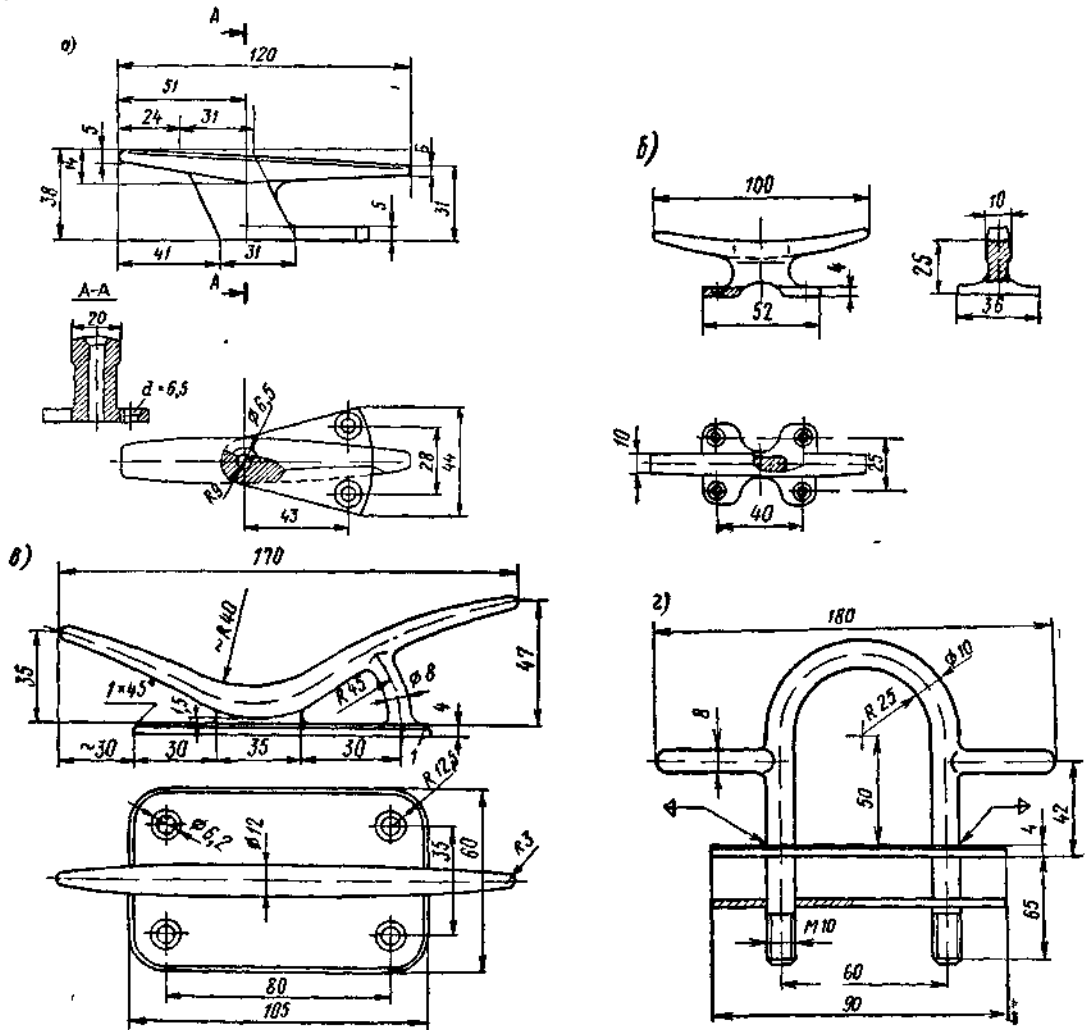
Утки литые (а и б) и сварной конструкции (в и г).
